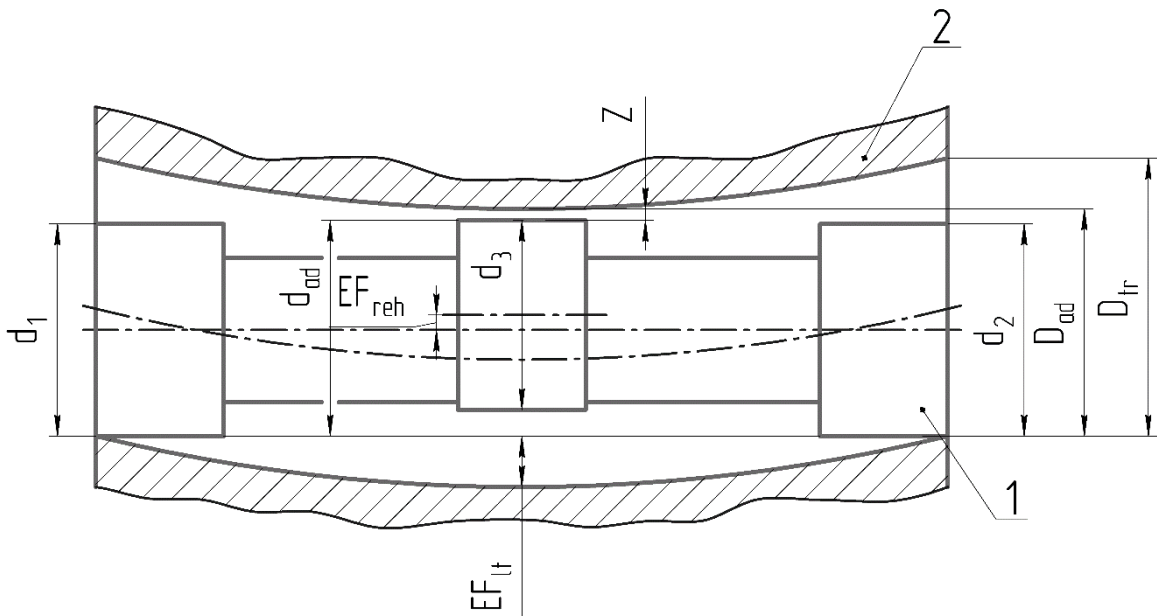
Схема положения корпуса ракетной части снаряда в пусковую направляющую:
